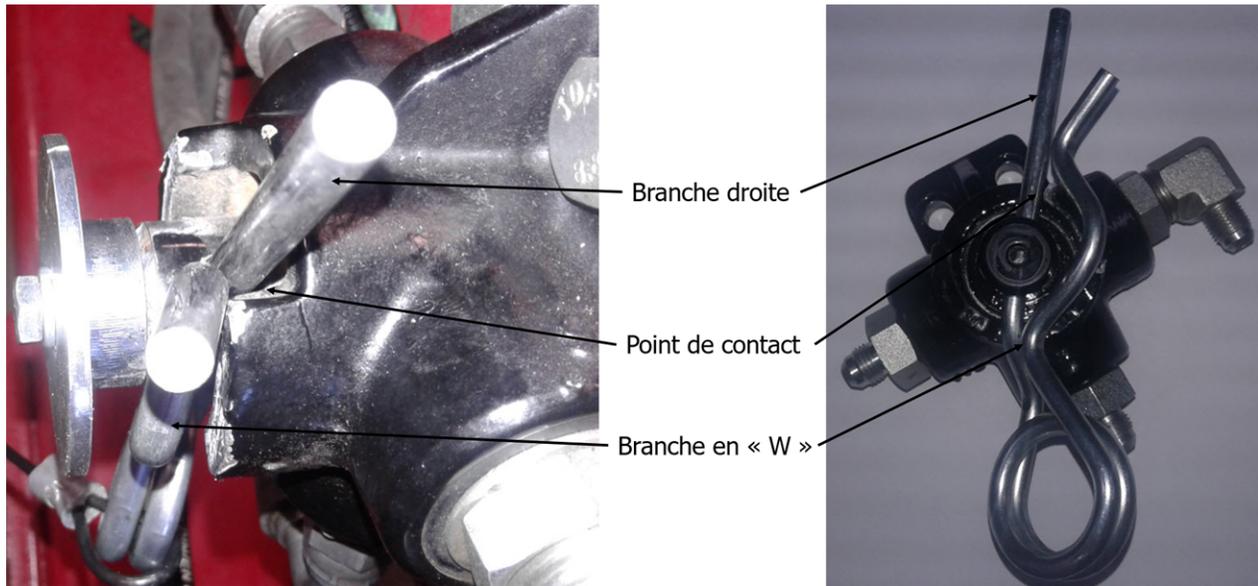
Goupille et valve d'urgence des freins hydrauliques
